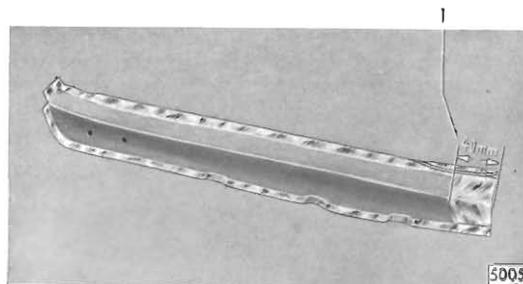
Flansch des neuen Hinterlängsträger-Hinterteiles beiderseits blankgesäubert
